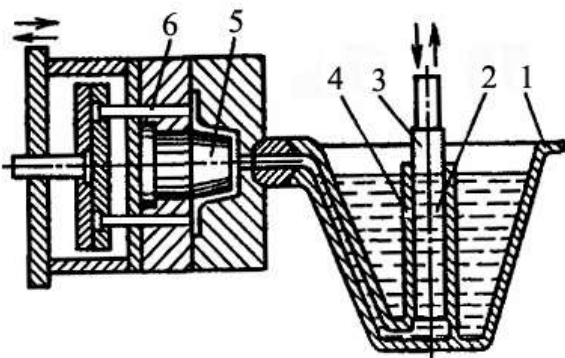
Виготовлення виливків литтям під тиском на машині з гарячою камерою пресування
